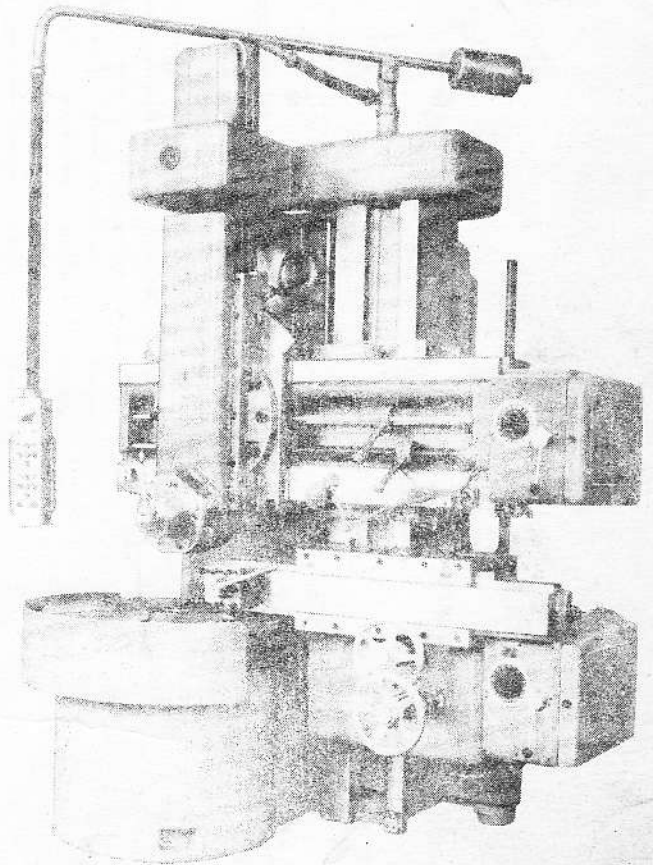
Общий вид токарно-карусельного станка модели I53IM
